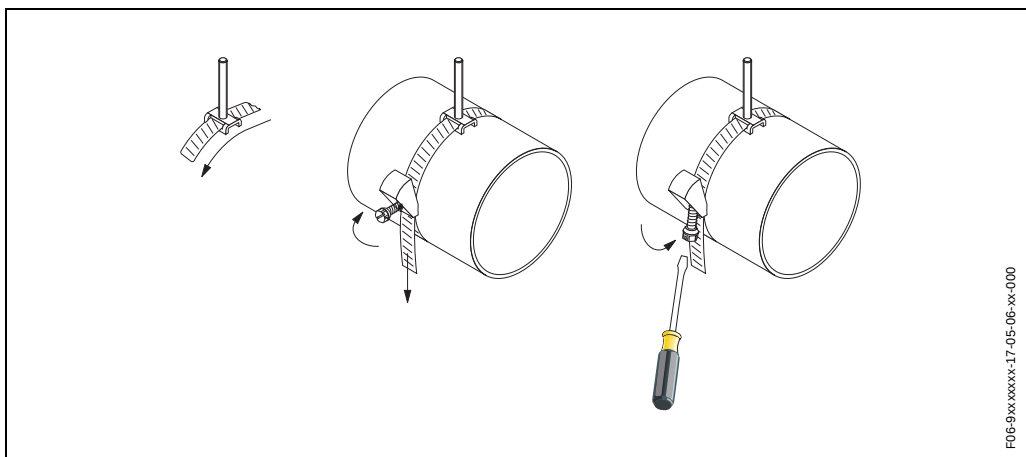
Установка натяжного обруча для трубы ДУ 50...200
